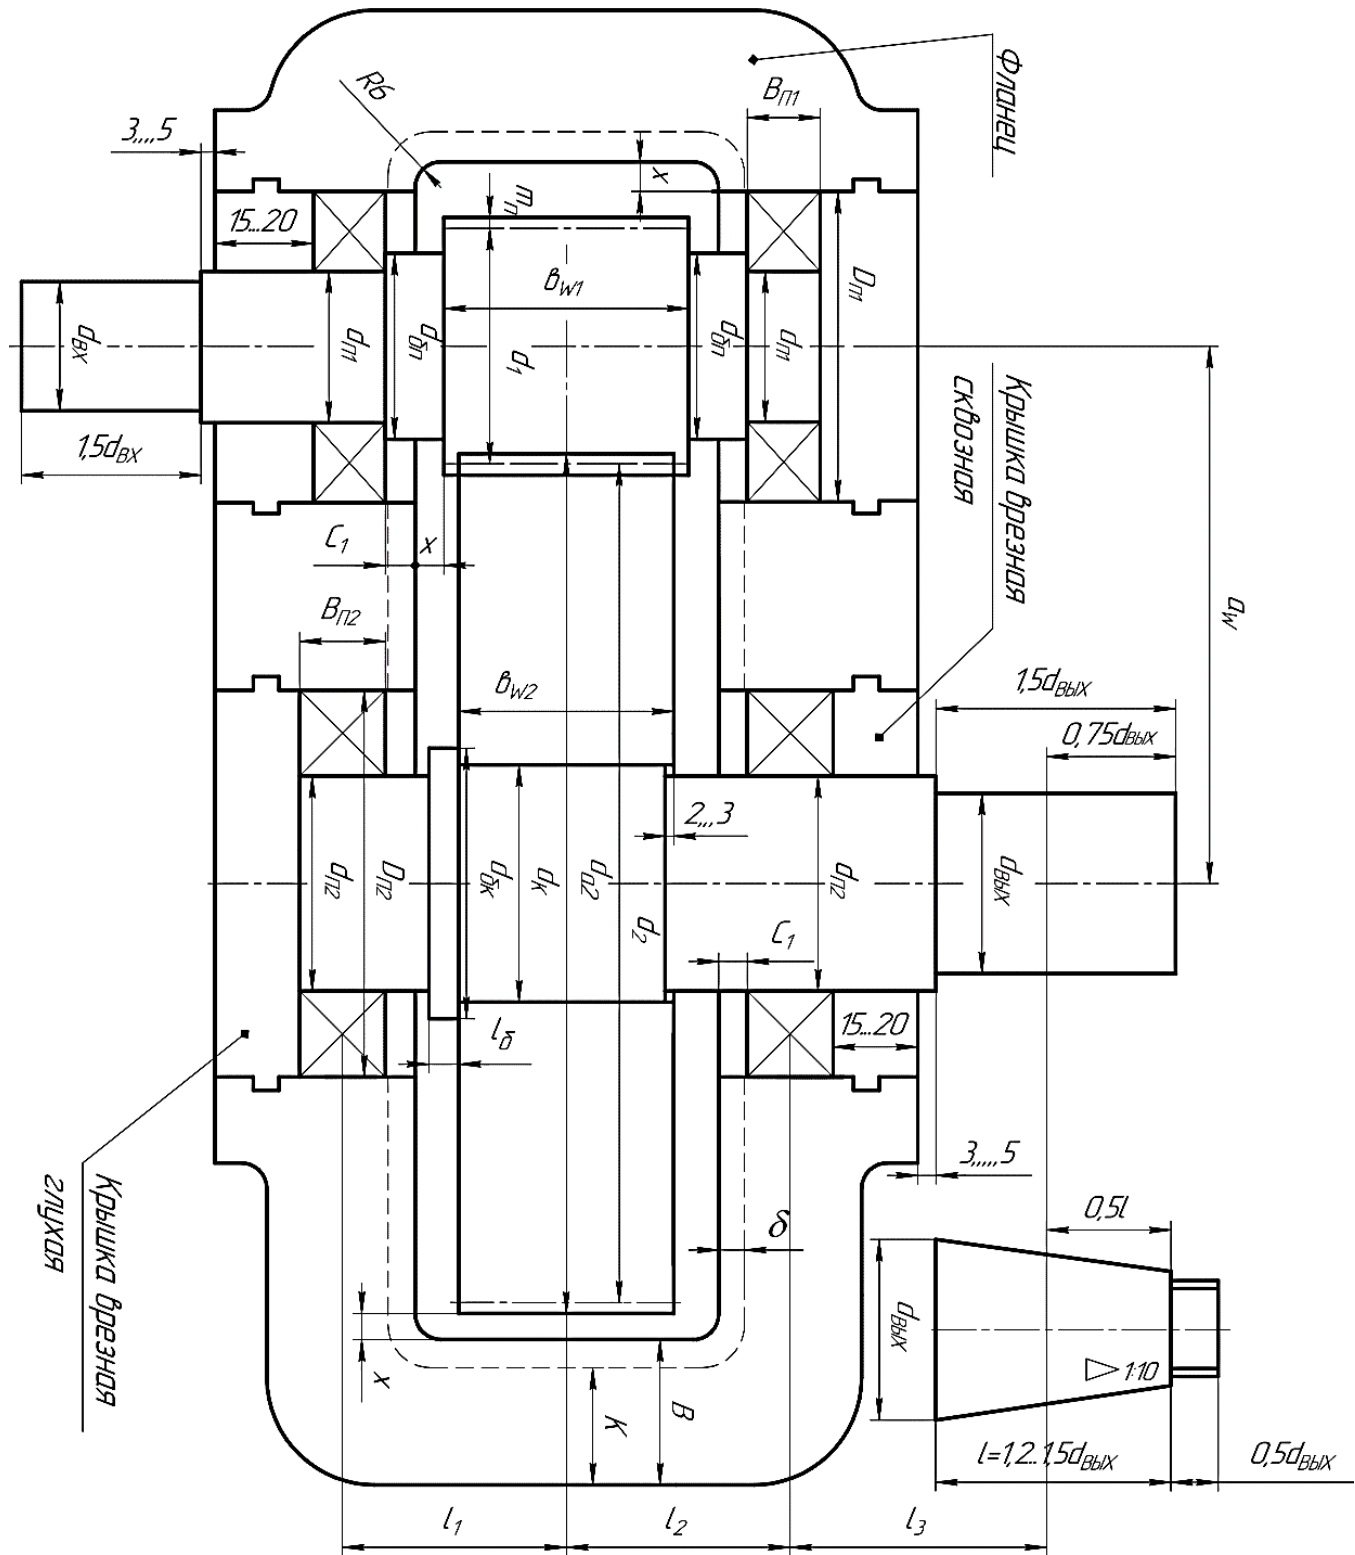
Второй этап эскизной компоновки одноступенчатого цилиндрического редуктора
